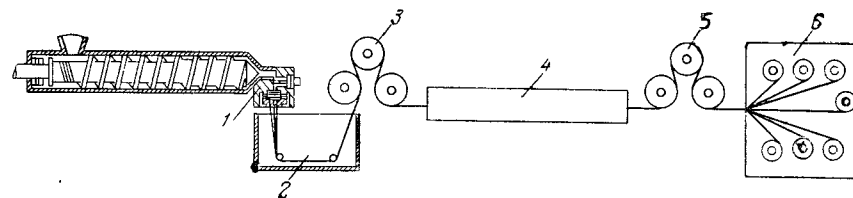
Схема агрегата для получения моноволокна из полиолефинов: 1—прядильная головка; 2—ванна для охлаждения волокна; 3, 5—вальцы; 4—вытяжная камера; 6—приемное устройство.
